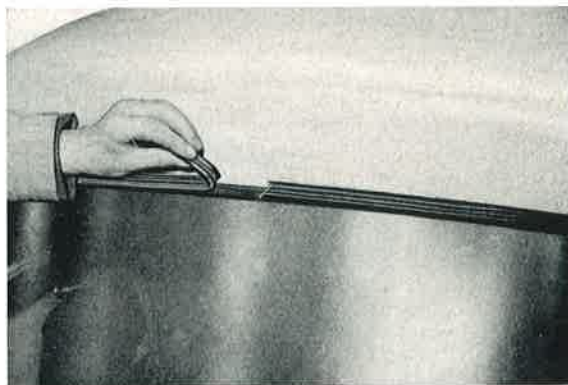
Am Einschnitt beginnend wird die Außenlippe des Gummirahmens ringsherum vorsichtig abgerissen.
